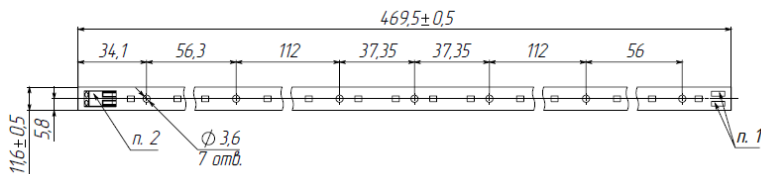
Внешний вид с габаритными и присоединительными размерами СДПП TRN-Line-09W-18-2835-0902 серии FLASH
